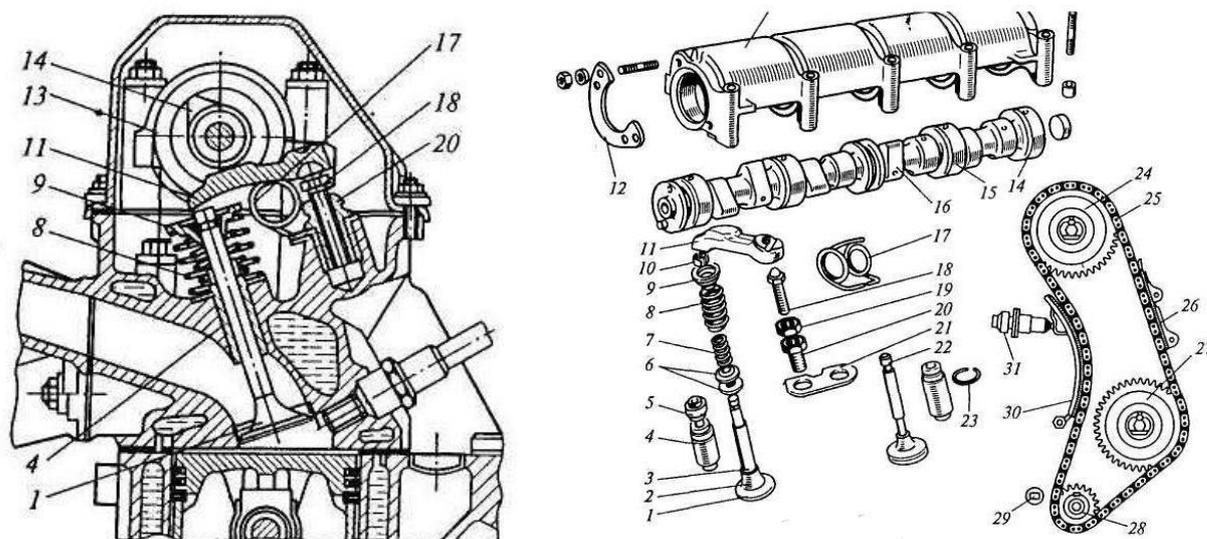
Газораспределительный механизм с верхним расположением клапанов и распределительного вала с цепным приводом: 1, 22 — клапаны; 2 — головка; 3 — стержень; 4, 20 — втулки; 5 — колпачок; 6 — шайбы; 7, 8, 17 — пружины; 9 — тарелка; 10 — сухарь; 11 — рычаг; 12 — фланец; 13 — корпус; 14 — распределительный вал; 15 — шейка; 16 — кулачок; 18 — болт; 19 — гайка; 21 — пластина; 23 — кольцо; 24, 27, 28 — звездочки; 25 — цепь; 26 — успокоитель; 29 — палец; 30 — башмак; 31 — натяжное устройство
